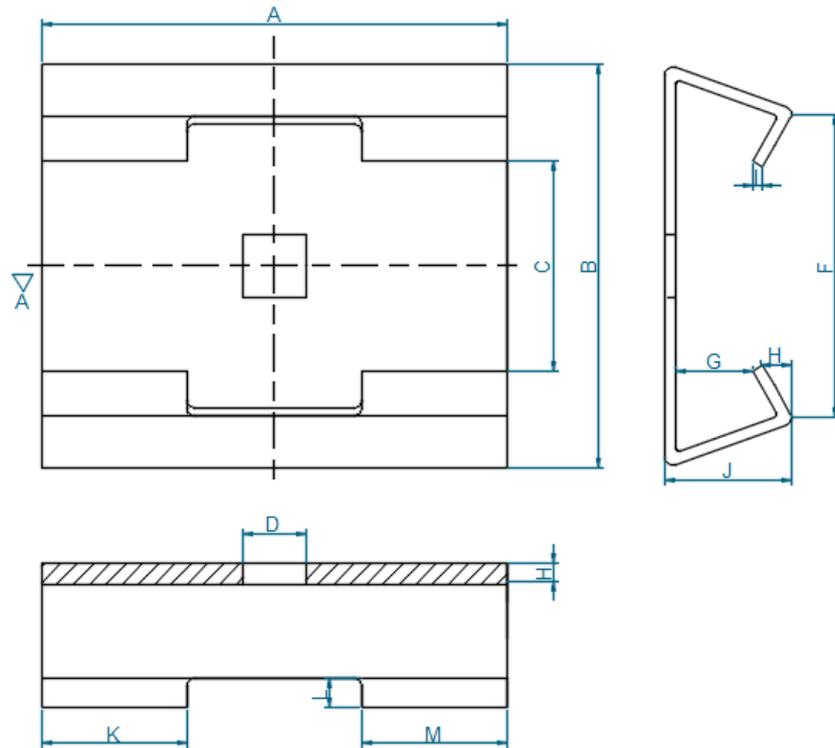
Dimensiones Físicas de un Asiento para Cruceta.
